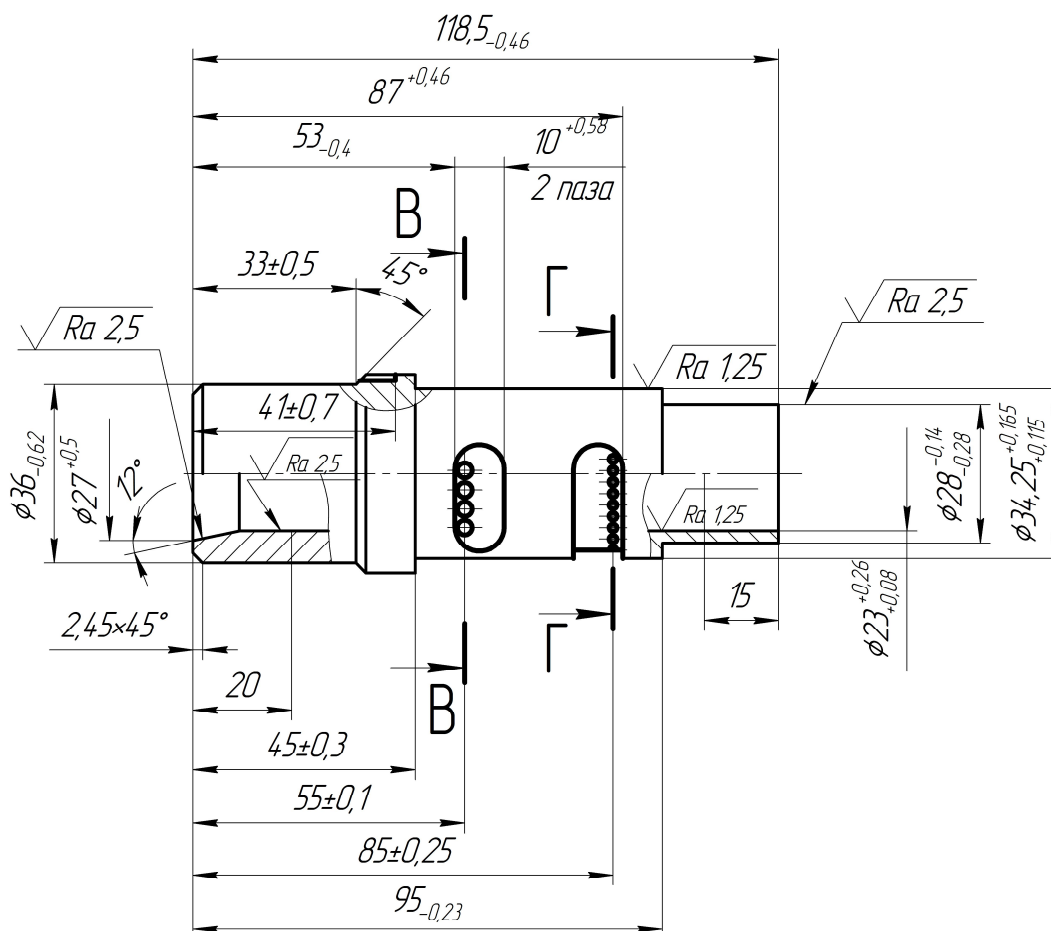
Креслення оброблювальної деталі «Втулка»
